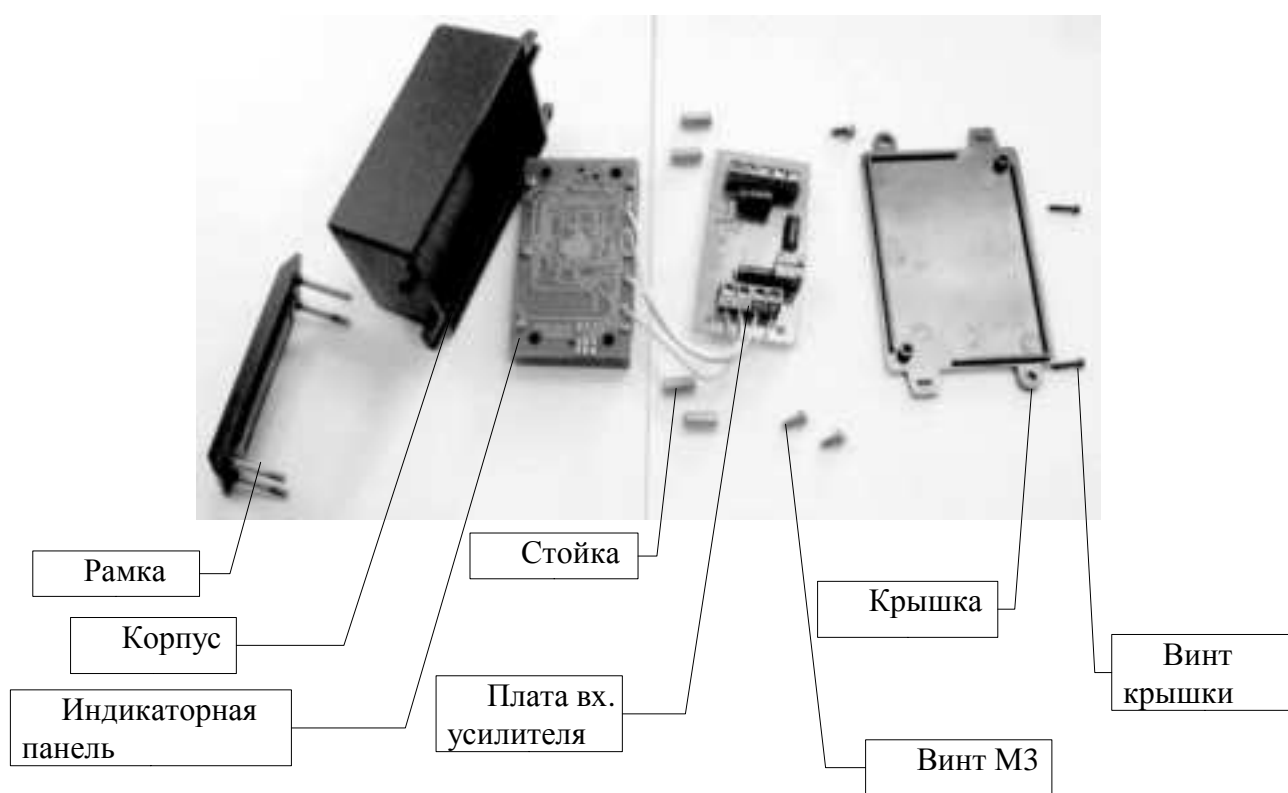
Разборка изделия для монтажа на наружную поверхность шкафа.
